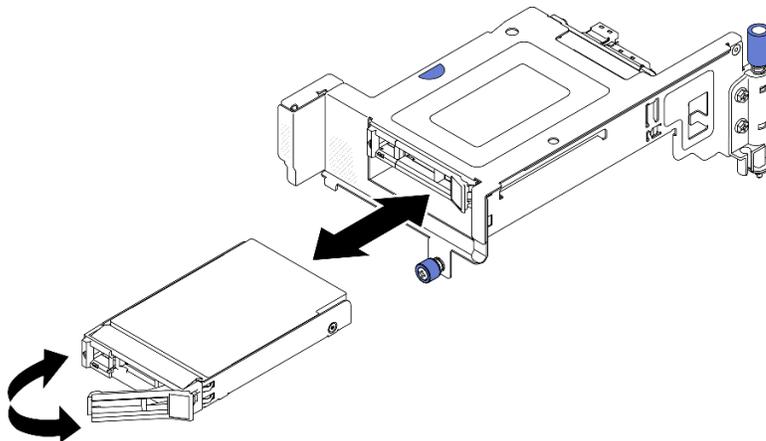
Entfernen der Hot-Swap-Laufwerke
